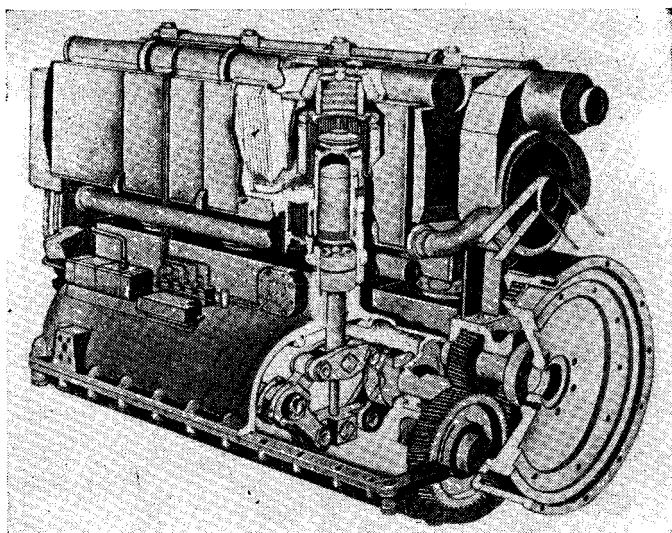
Общий вид четырехцилиндрового однорядного двигателя Стирлинга модели 4-235.
